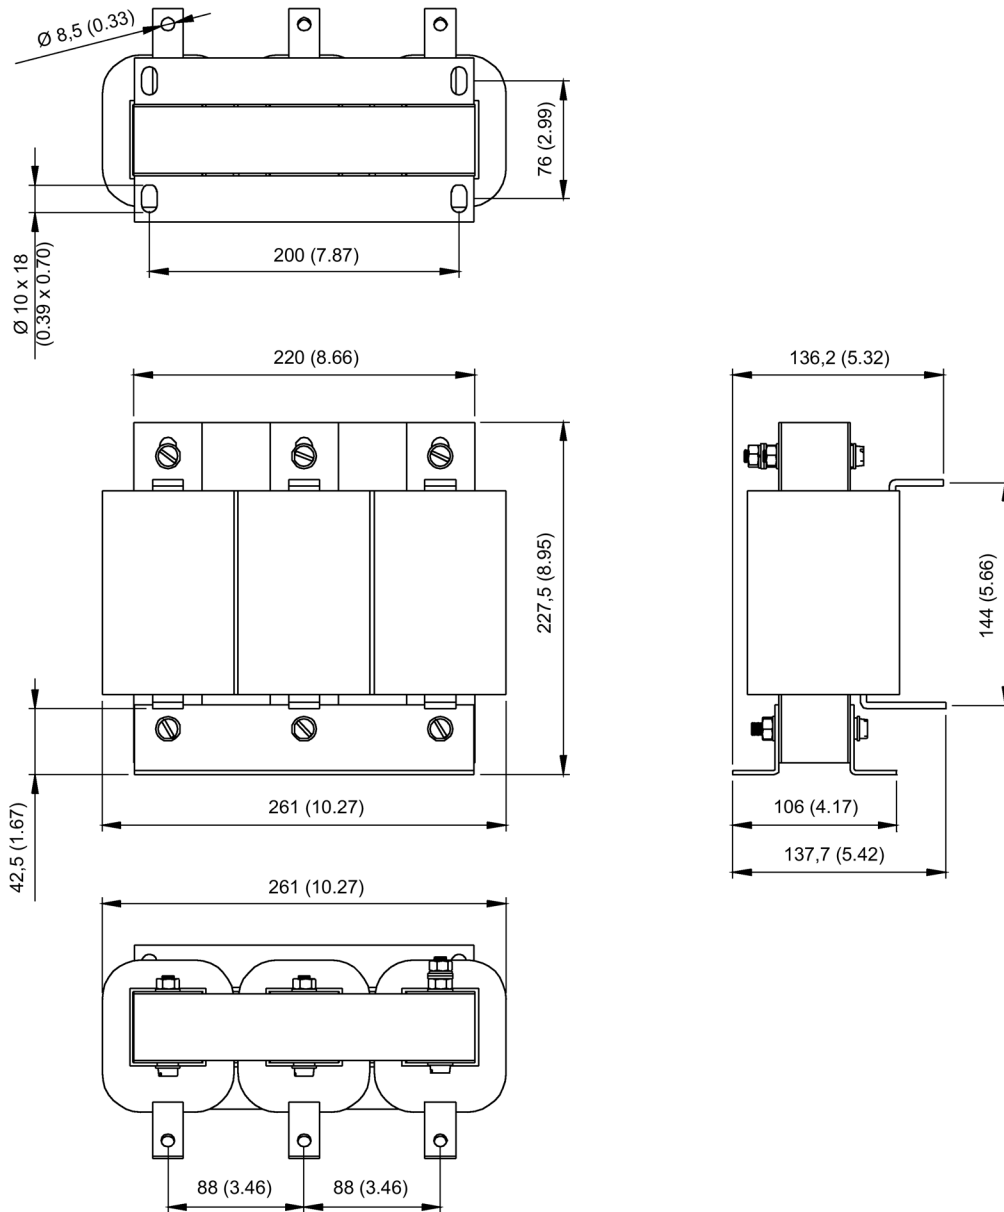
Croquis acotado de una bobina de red para Basic Line Module de 100 kW, todas las medidas en mm y (pulgadas)
